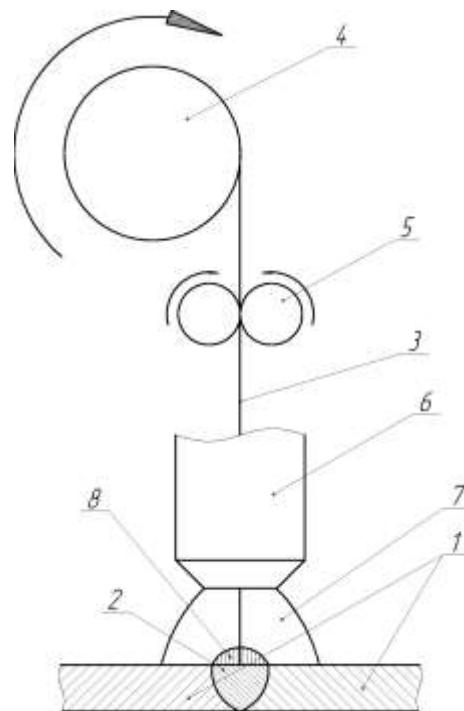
Схема напівавтоматичного зварювання в захисному газі
